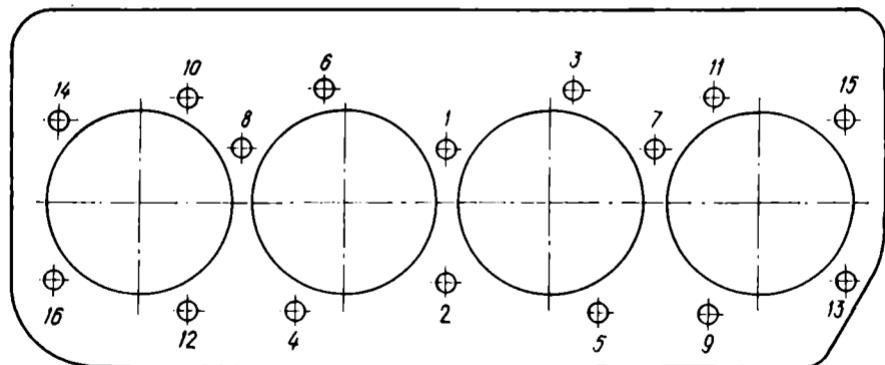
Последовательность затяжки болтов крепления головки цилиндров.
